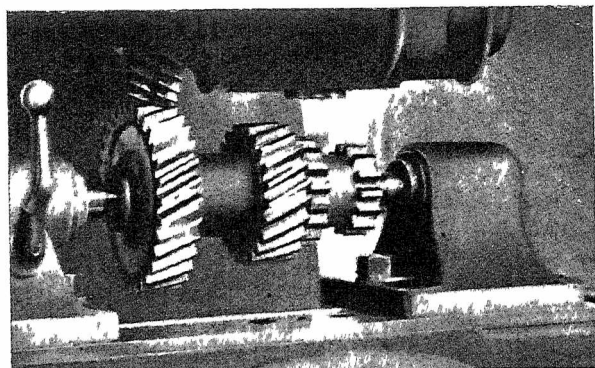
Przykład koła zębatego o pozarywanej powierzchni flankowej zębów, wskutek szybkiego stępienia się narzędzia podczas obróbki b. twardego materiału, z prawej strony — także koło po rolowaniu
